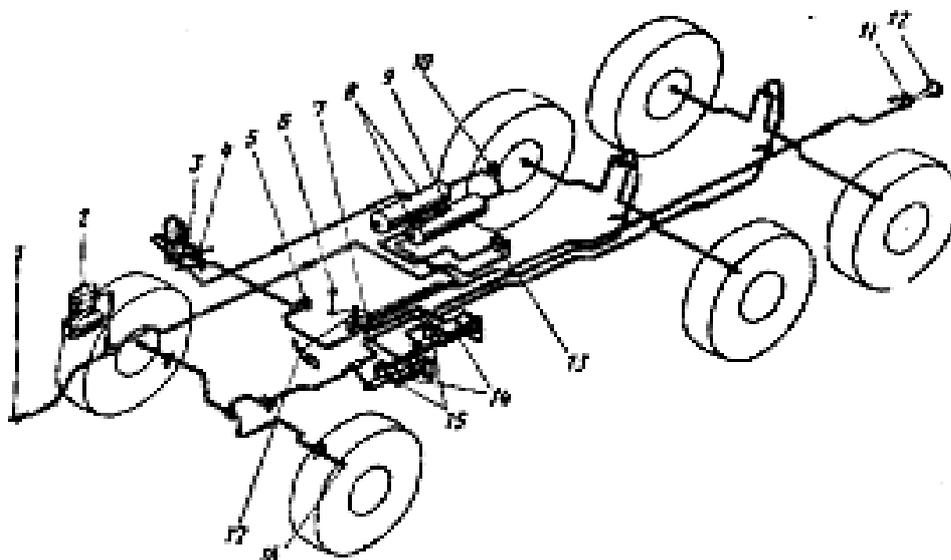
Схема компоновки приборов пневмогидравлического привода тормозов. 1-буксирный клапан, 2-компрессор, 3-крестовина, 4-кран отбора воздуха, 5-манометр, 6-рычаг управления стояночным тормозом, 7-тормозной кран, 8-воздушные баллоны, 9-датчик давления, 10-межбаллонный редуктор, 11-раздаточный кран, 12-соединительный привод, 13-регулятор давления, 14-пневмоусилитель, 15-главные тормозные цилиндры, 16-подвод к колесному цилиндру, 17-педаля привода рабочей тормозной системы
